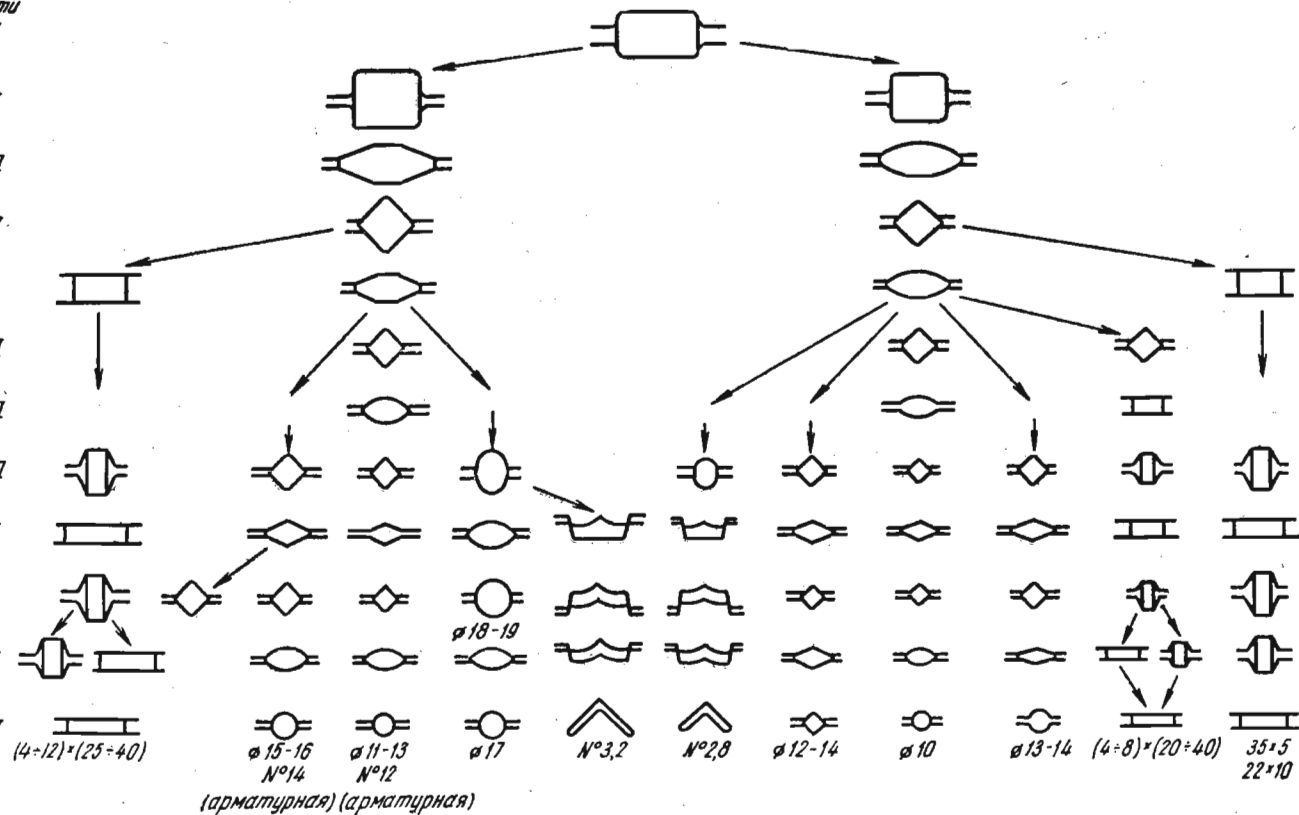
Принципиальная схема калибровки валков мелкосортного стана
